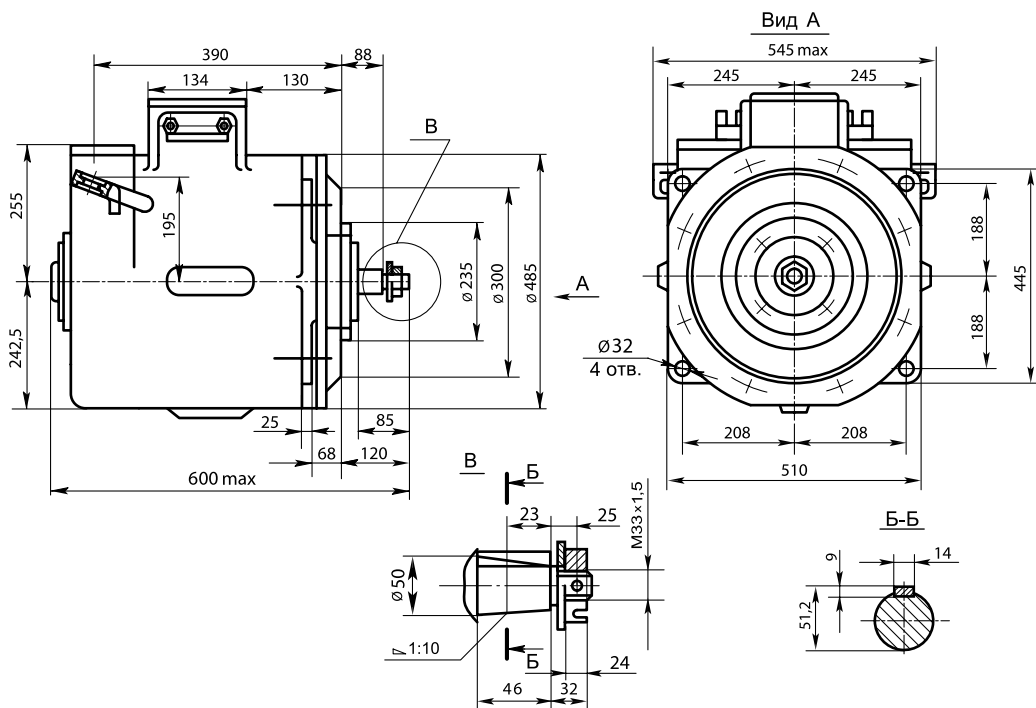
Габаритные и установочные размеры электродвигателя ДРТ-13М
